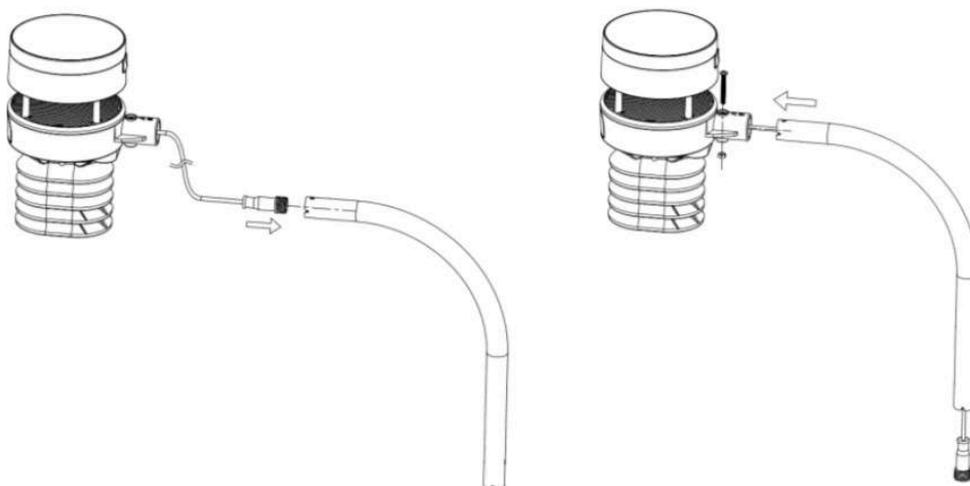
schema di montaggio del pacchetto del sensore 5-2. 15
